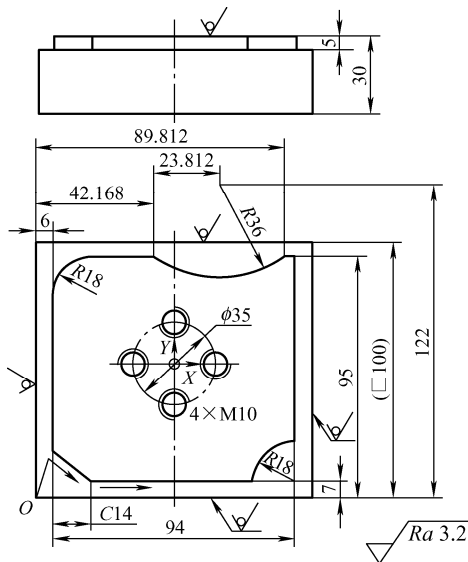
平面零件的轮廓铣削及螺纹孔加工
